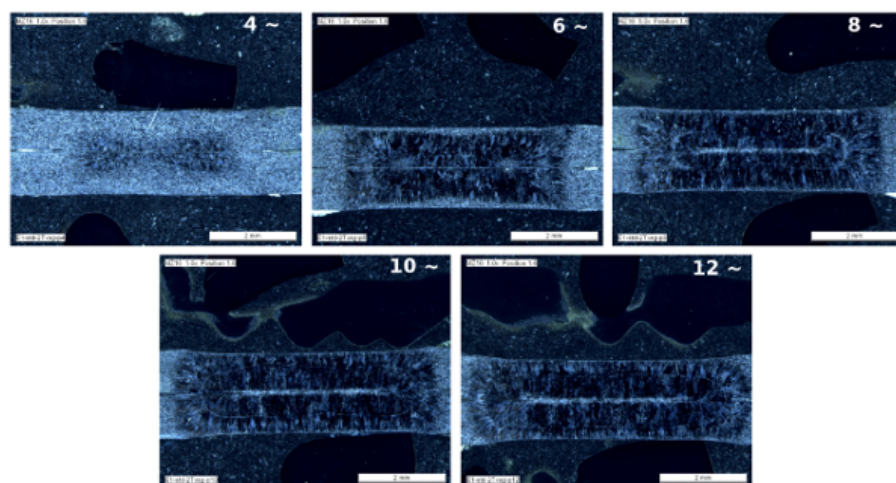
Cinétique expérimentale de développement du noyau - assemblage 2T XSG 1mm/1mm - 100 points soudés.
